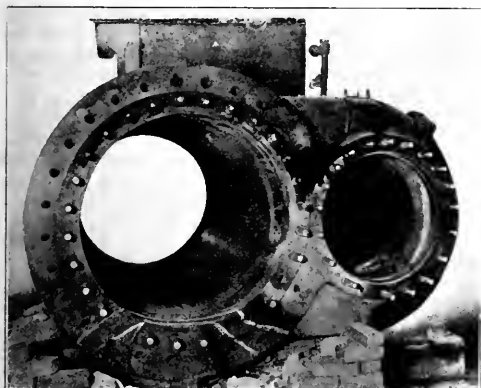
BRIDA SOLDADA EN EL CILINDRO DE ALTA PRESIÓN DE CINCO TONELADAS Y 1,35 METROS DE LARGO
